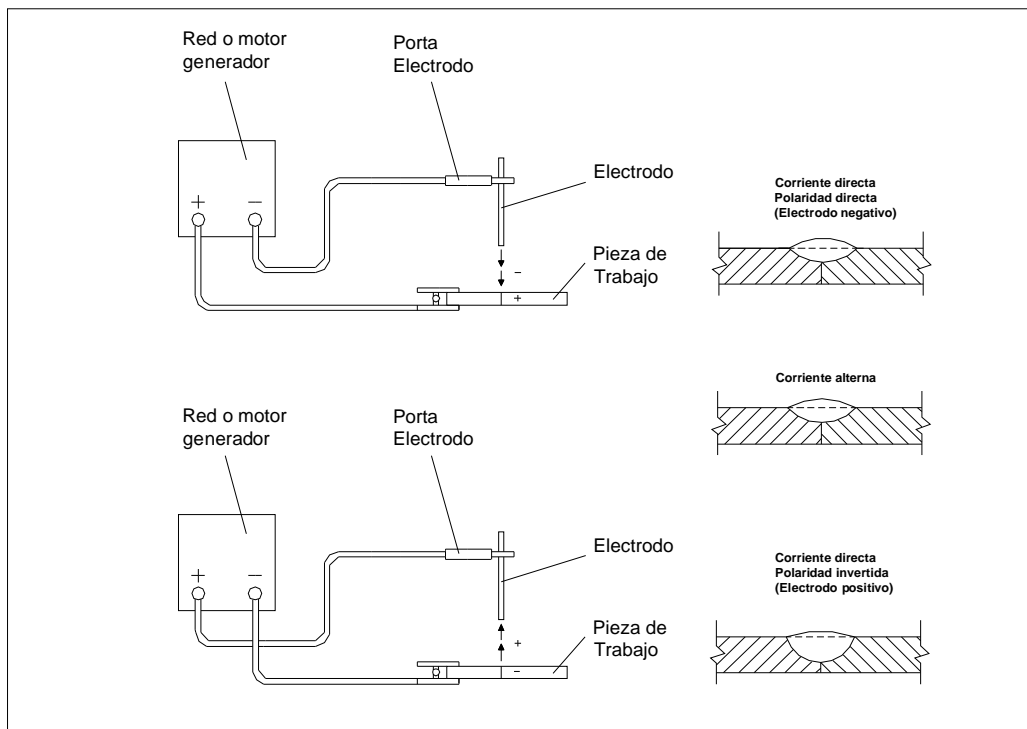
Efecto de la corriente directa (polaridad directa e invertida) y alterna en una unión de soldadura. (SOLDADURA, APLICACIONES Y PRACTICAS, Henry Horwitz, P.E.1997, capítulos 4 y 5, Pág. 53, 119).
